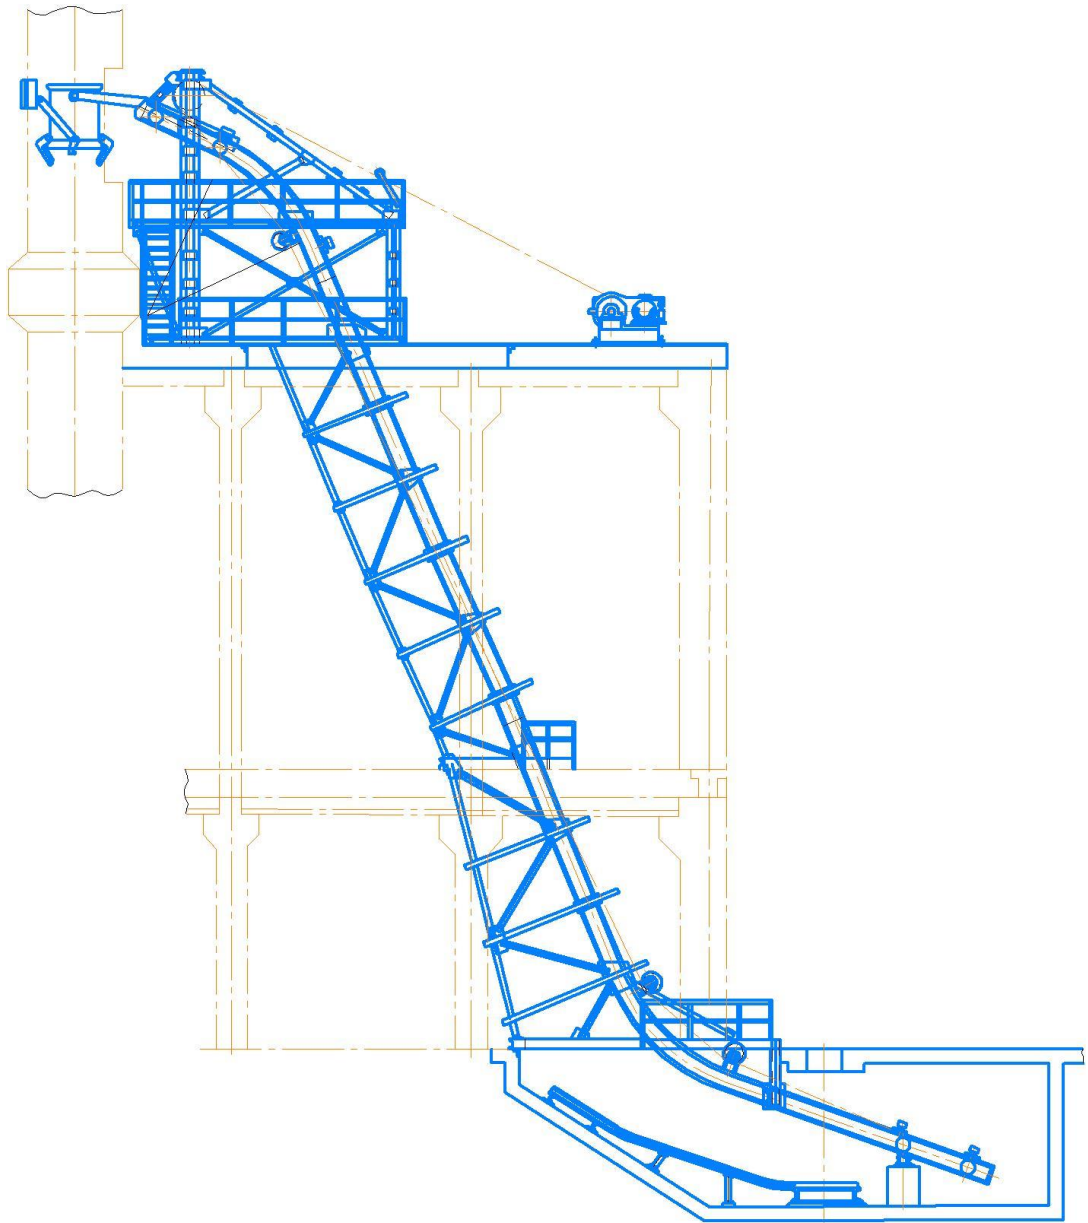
Схема баддьевого підйомника ливарного цеху
